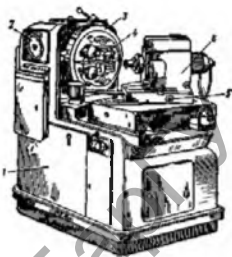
Зубострогальный полуавтомат мод. 5Т23В для обработки прямозубых конических колес
